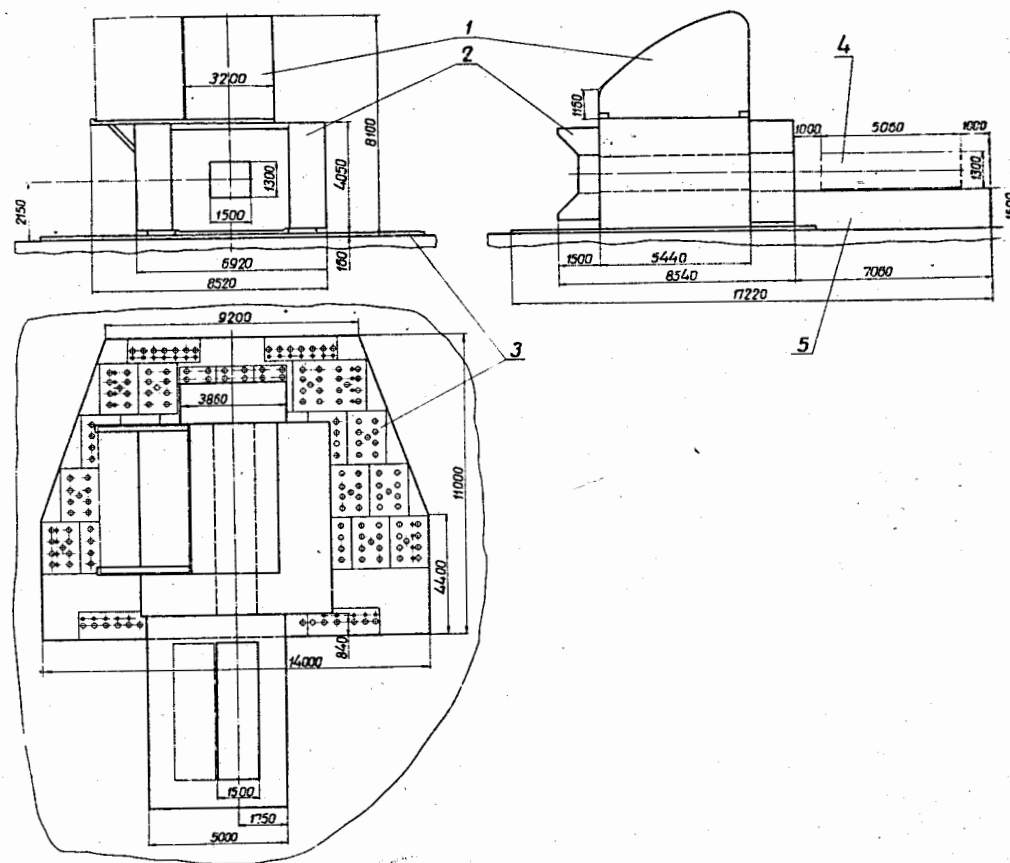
Общий вид магнита СП-136. 1 - ферма для крепления зеркал, 2 - электромагнит СП-136, 3 - плита фундаментная, 4 - тележка с искровыми камерами, 5 - ферма опорная.
